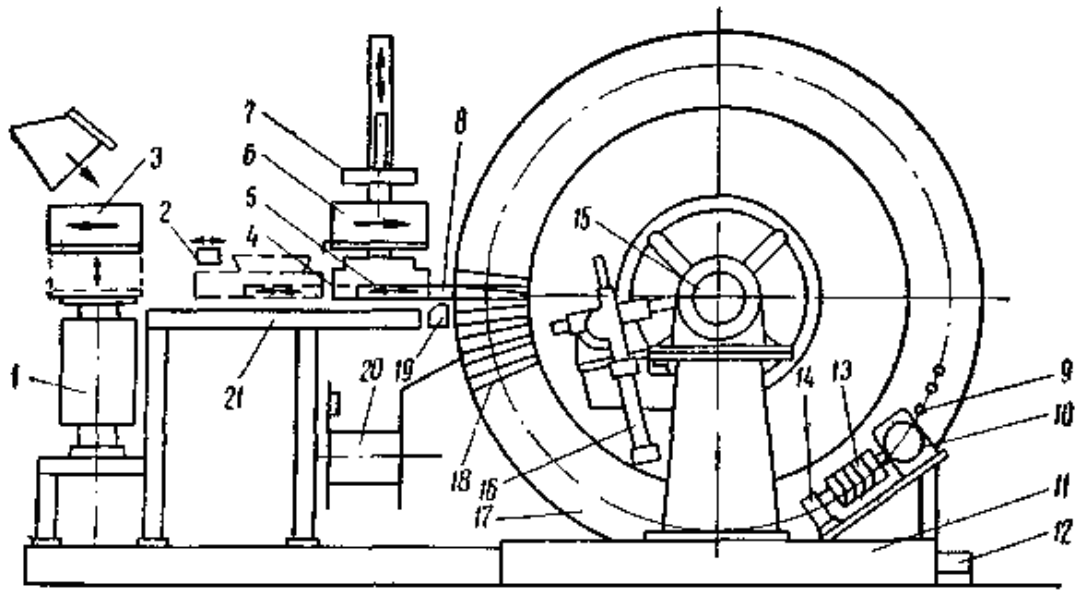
Роторний морозильний апарат «Кюльавтомат»: 1 – ваги; 2 – пристрій витягування; 3 – дозуючий пристрій; 4 – касети; 5 – штовхач; 6 – заслінка; 7 – затвор; 8 – поліетиленові листи; 9 – штифти; 10 – редуктор; 11 – рама; 12 – піддон; 13 – текстолітовий кулачок; 14 – гідравлічний привід ротора; 15 – пустотілий вал ротора; 16 – механізм розвантаження; 17 – кожух; 18 – морозильні плити; 19 – лотоки; 20 – транспортер розвантаження; 21 – розвантажувальний пристрій
